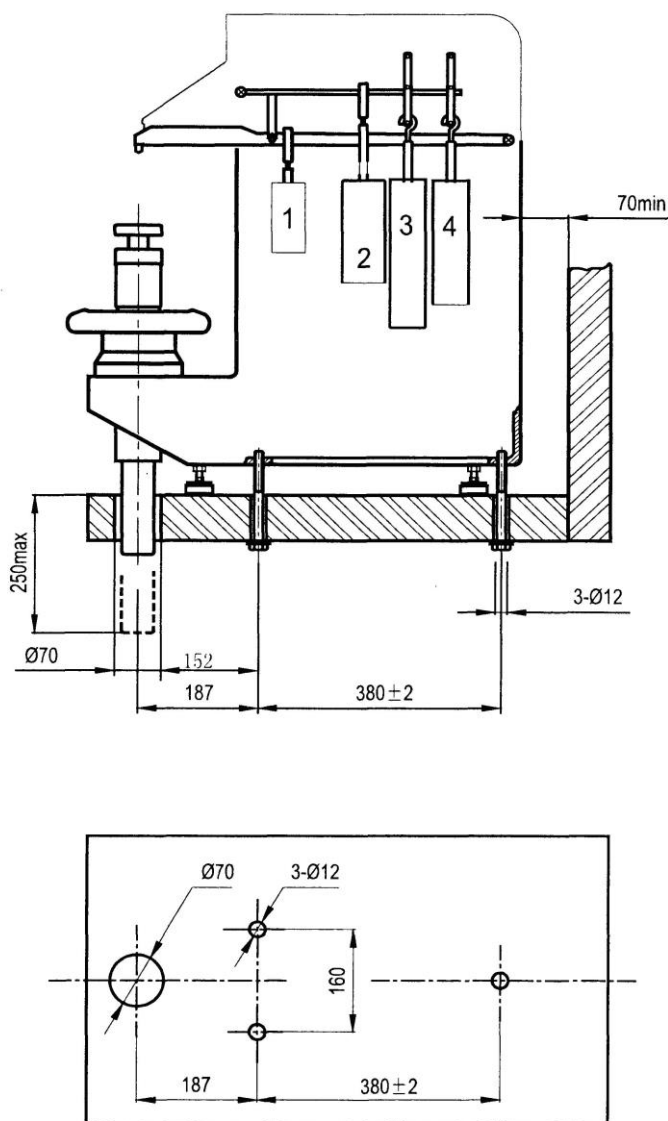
Схема установки твердомеров моделей ТН300, ТН301, ТН310
